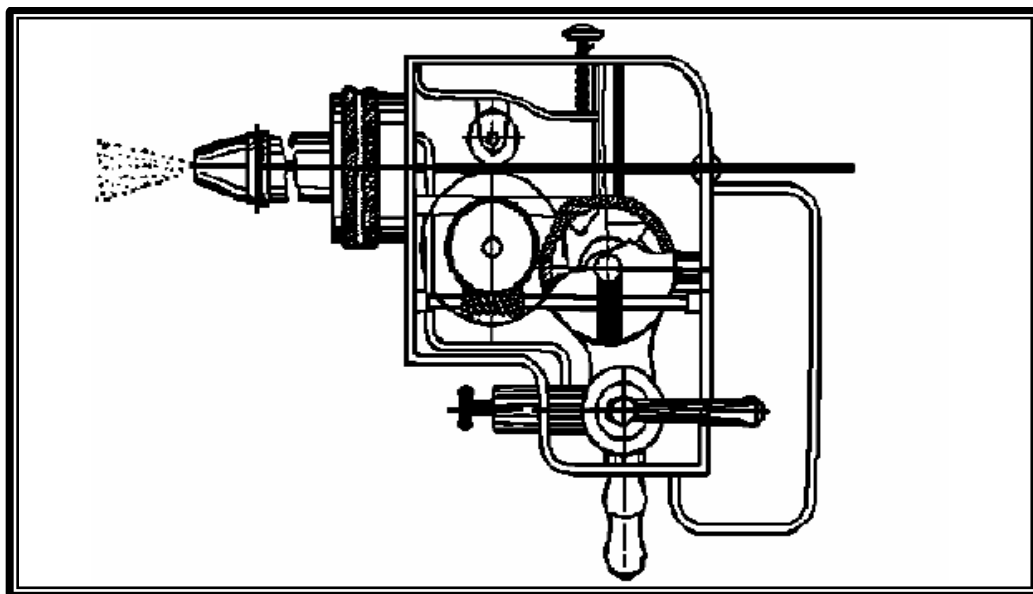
Sección transversal de la primera pistola de aspersion por alambre [3].
